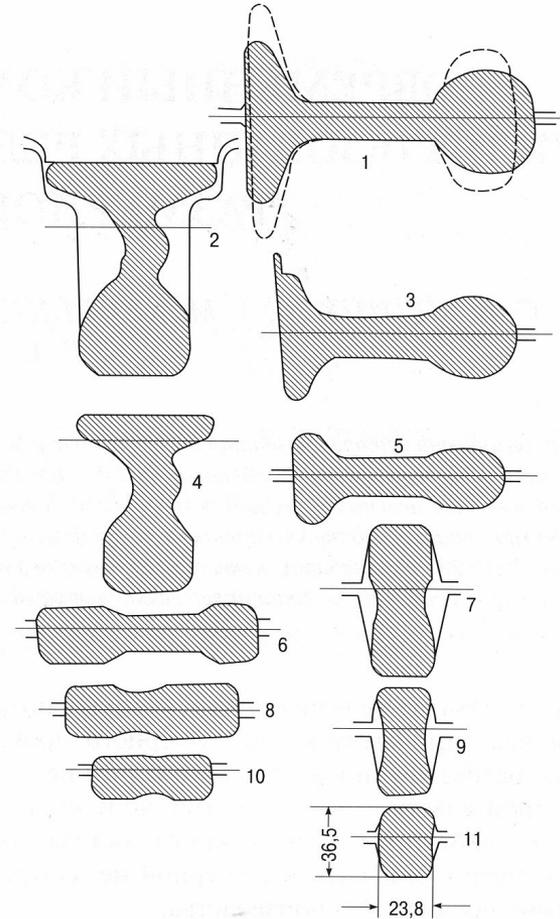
Схемы калибров валков для перековки рельсов в заготовку без предварительного деления
